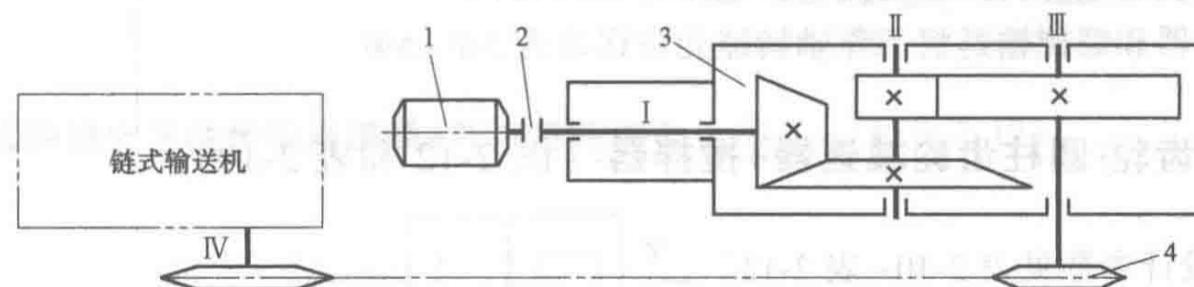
锥齿轮-圆柱齿轮减速器+滚子链传动
